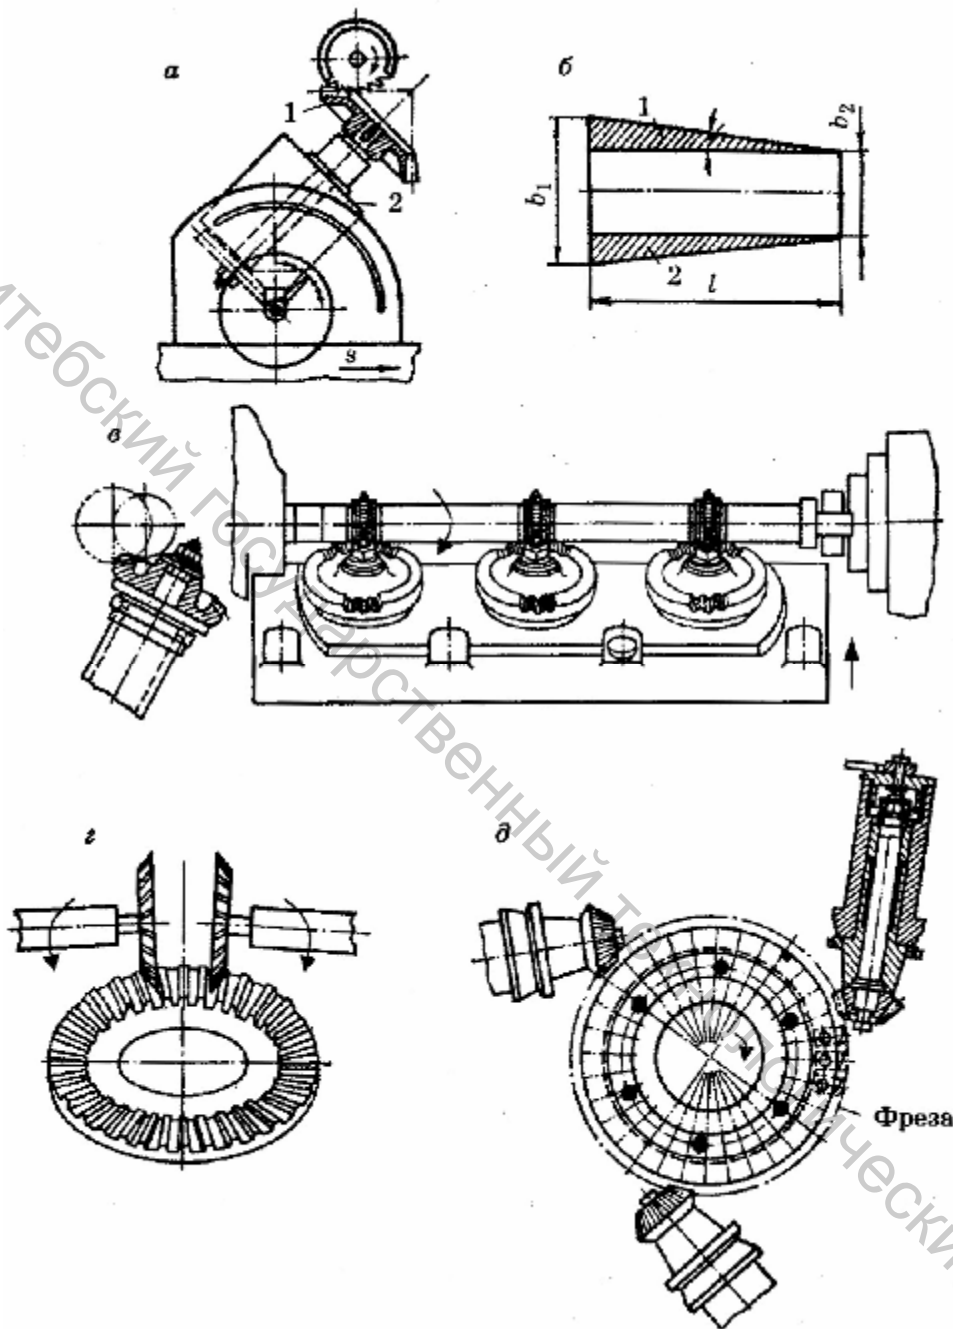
Зубофрезерование конического зубчатого колеса: а—установка заготовки на оправке; б— схема фрезерования впадины между зубьями; в— одновременно трех заготовок; г— одной заготовки двумя дисковыми фрезами; д— трех заготовок специальной дисковой фрезой
